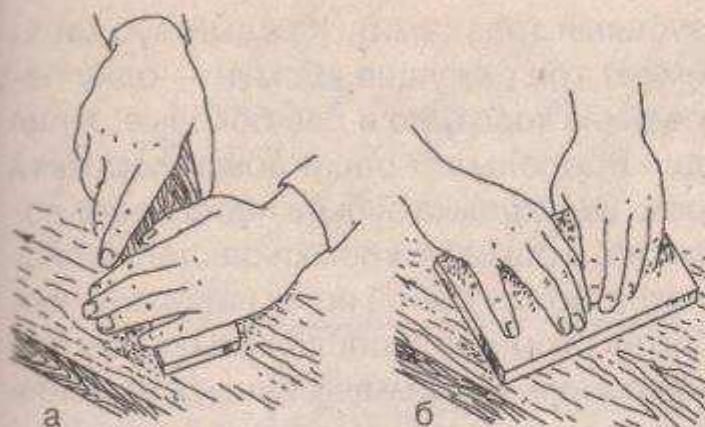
Положение рук при циклевании поверхности: а — обычной циклей; б — широкой циклей
